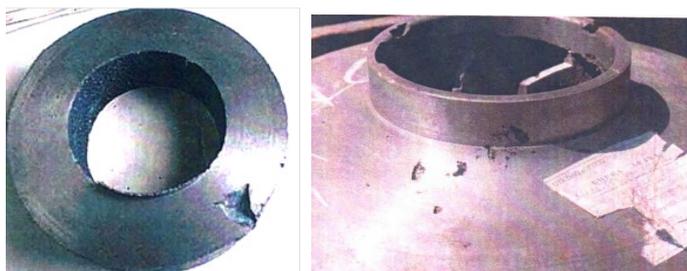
Дефект отливки Раковина усадочная закрытая
